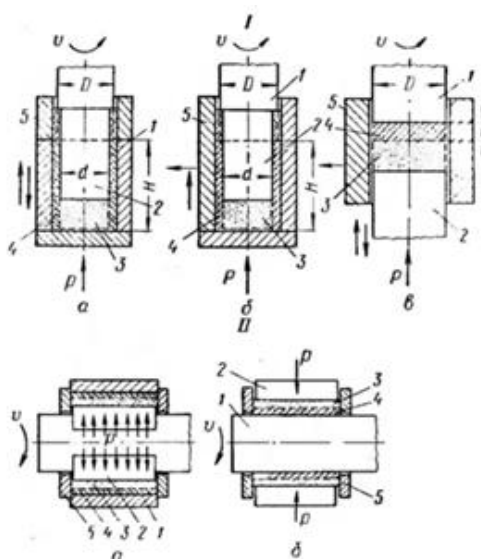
Принципиальные схемы процесса наплавки трением на внутреннюю (а), наружную (б) и торцевую (в) поверхности: 1 – деталь; 2 – инструмент; 3 – наплавляемый металл до наплавки; 4 – наплавленный металл; 5 - приспособление
